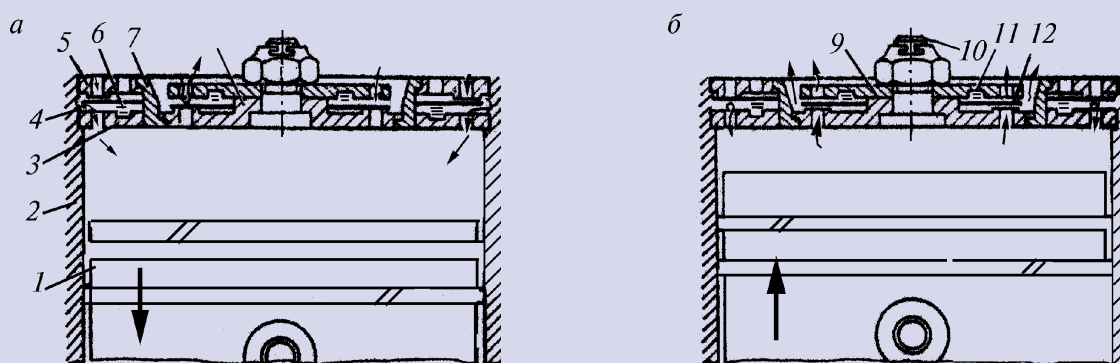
Схема работы клапанов компрессора: а — всасывание; б — нагнетание
